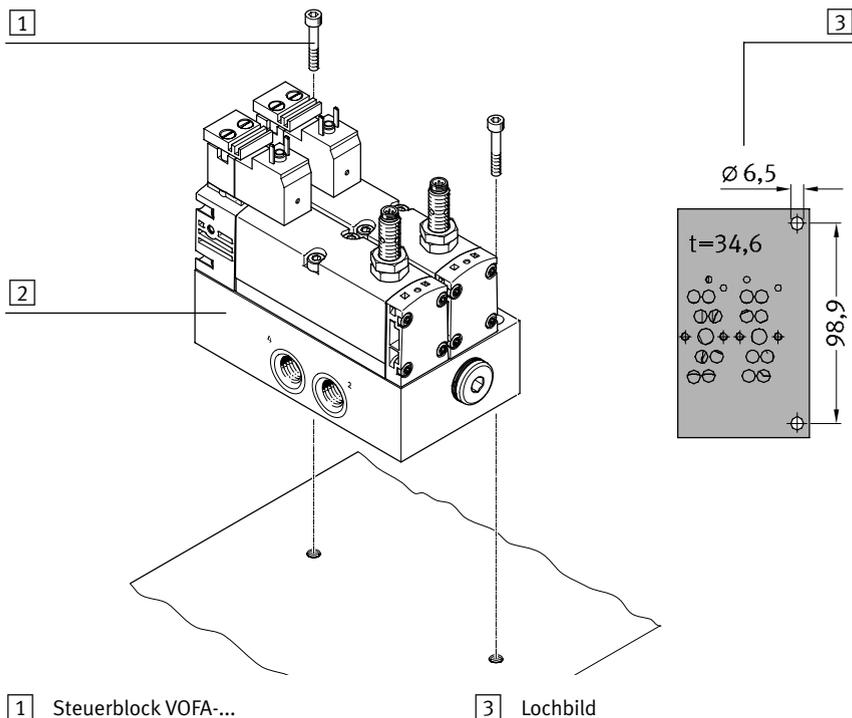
Befestigung/Montage der Einzelanschlussvariante
